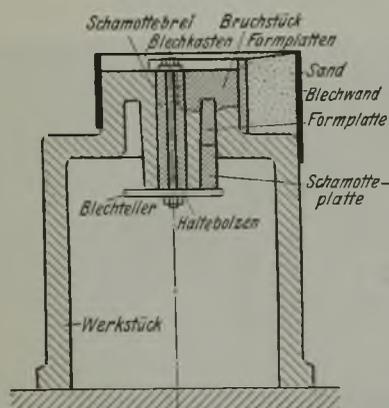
Einförmung eines Stückes für die Warschweißung.
